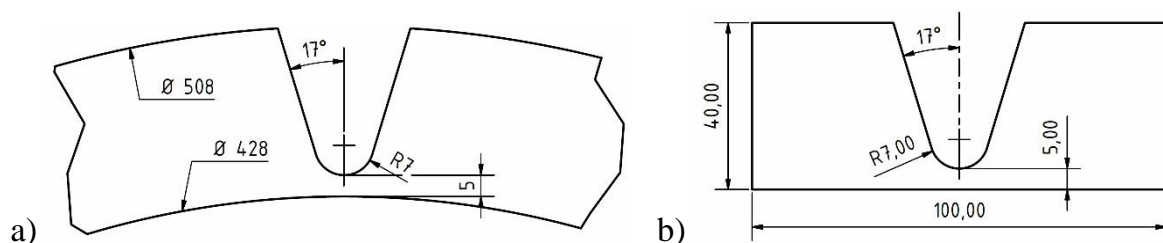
Fugengeometrie für Fülllagen a) Längsnahtrohr b) Schweißproben
